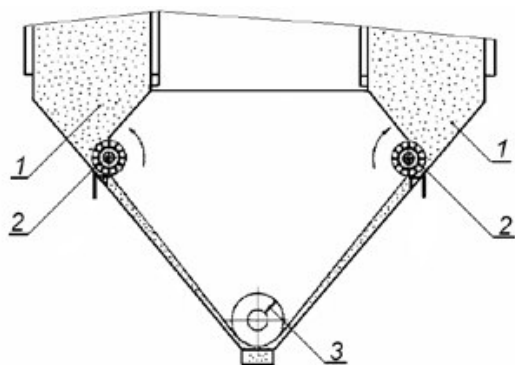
Выпускное устройство зерносушилки СЗК-20: 1 – сушильные колонки; 2 – роторы; 3 – шнек
